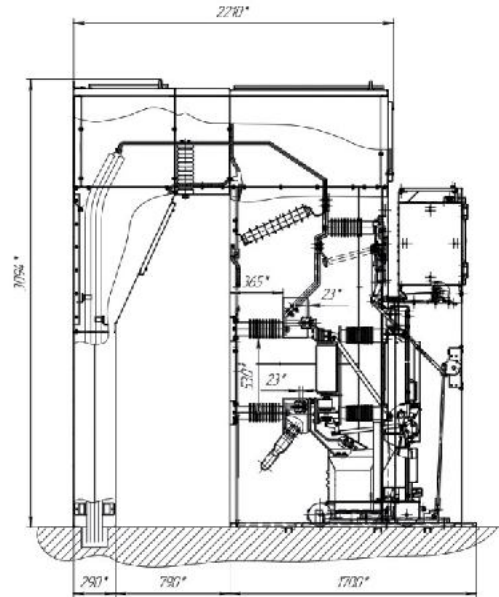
Шкаф с блоком кабельного ввода сквозь пол от стены здания РУ с возможностью присоединения 1, 2 кабелей на фазу.
